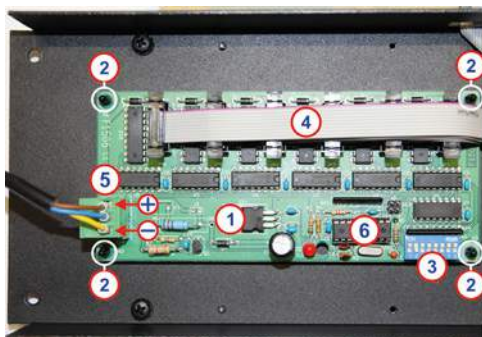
Ersetzen einer neuen FC DRIVER-Platine.
